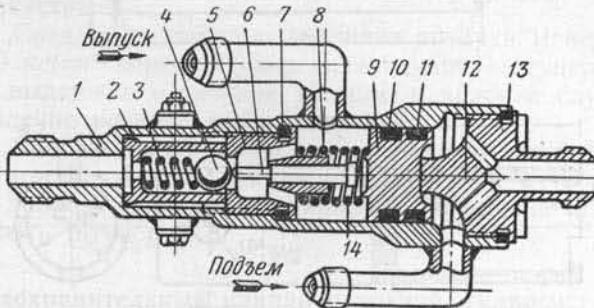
Распределительная коробка цилиндра уборки основной стойки шасси с тарельчатым клапаном.
